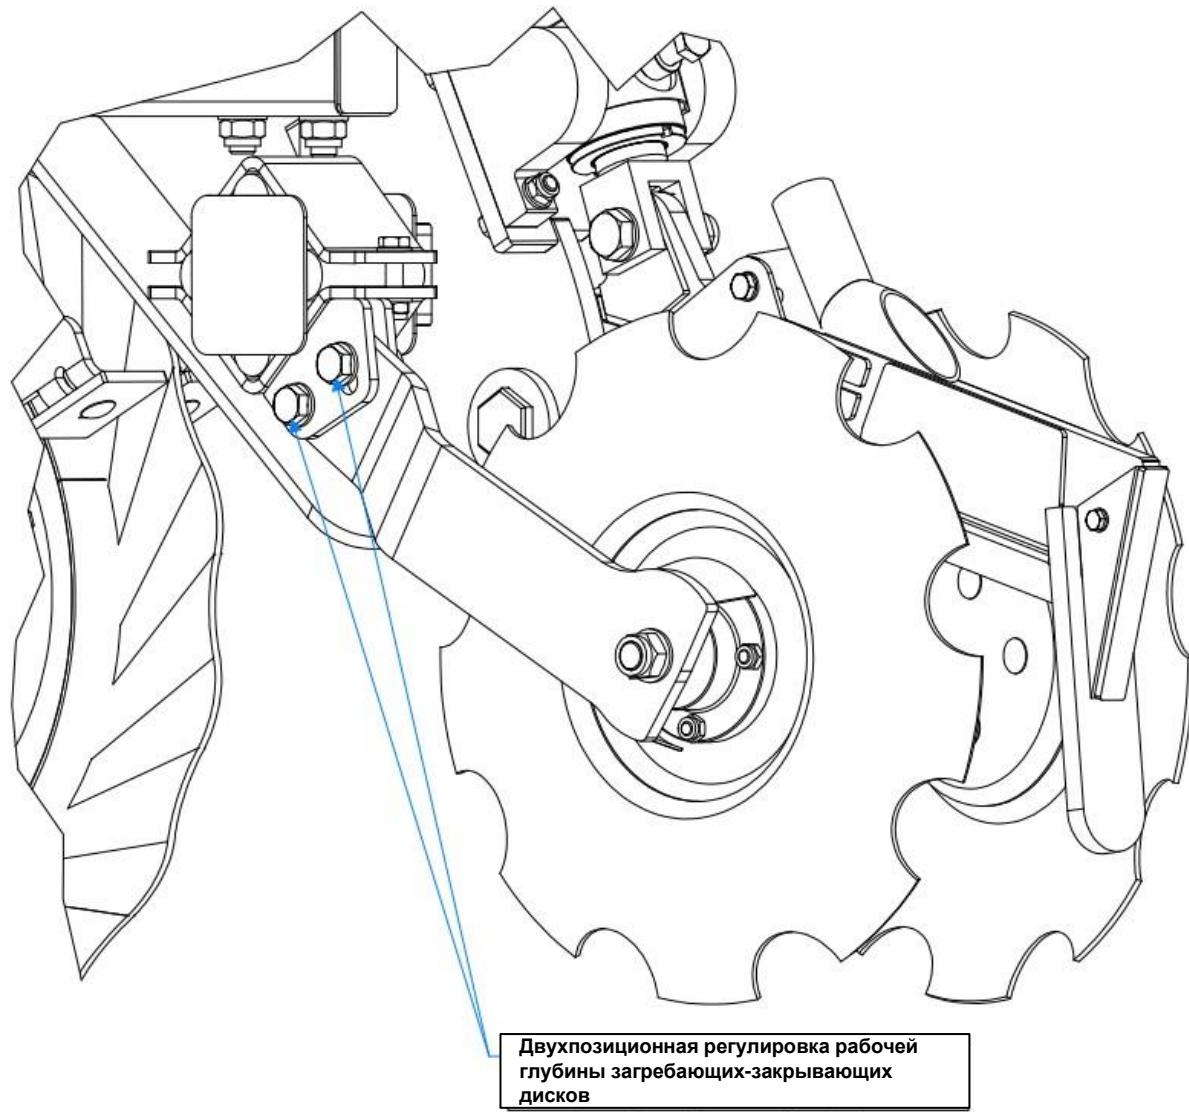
Способ регулировка рабочей глубины загребающего-закрывающего диска
